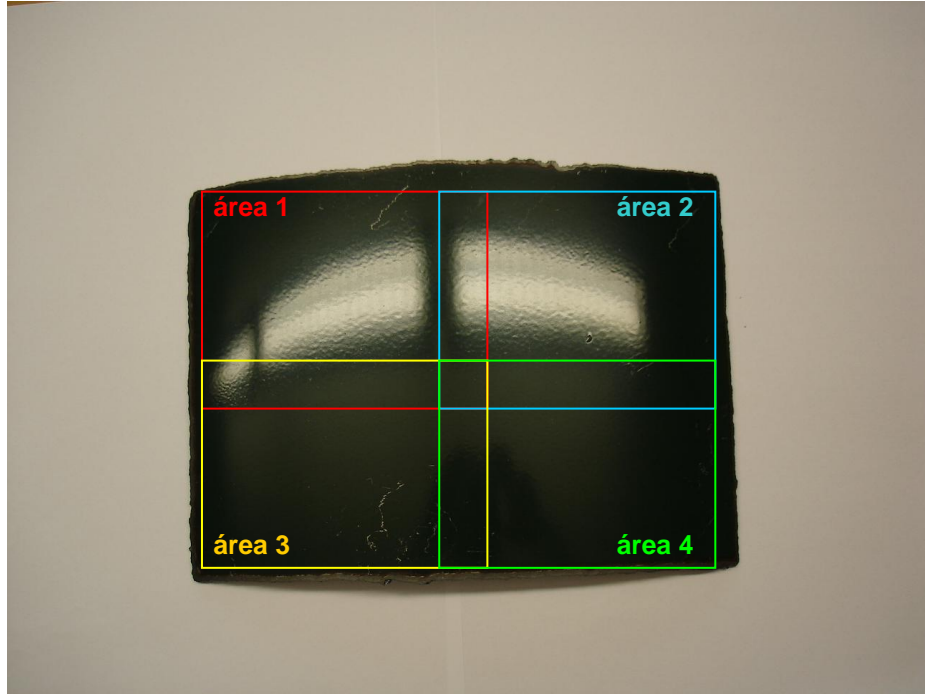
Esquema de inspeção da superfície frontal das amostras
